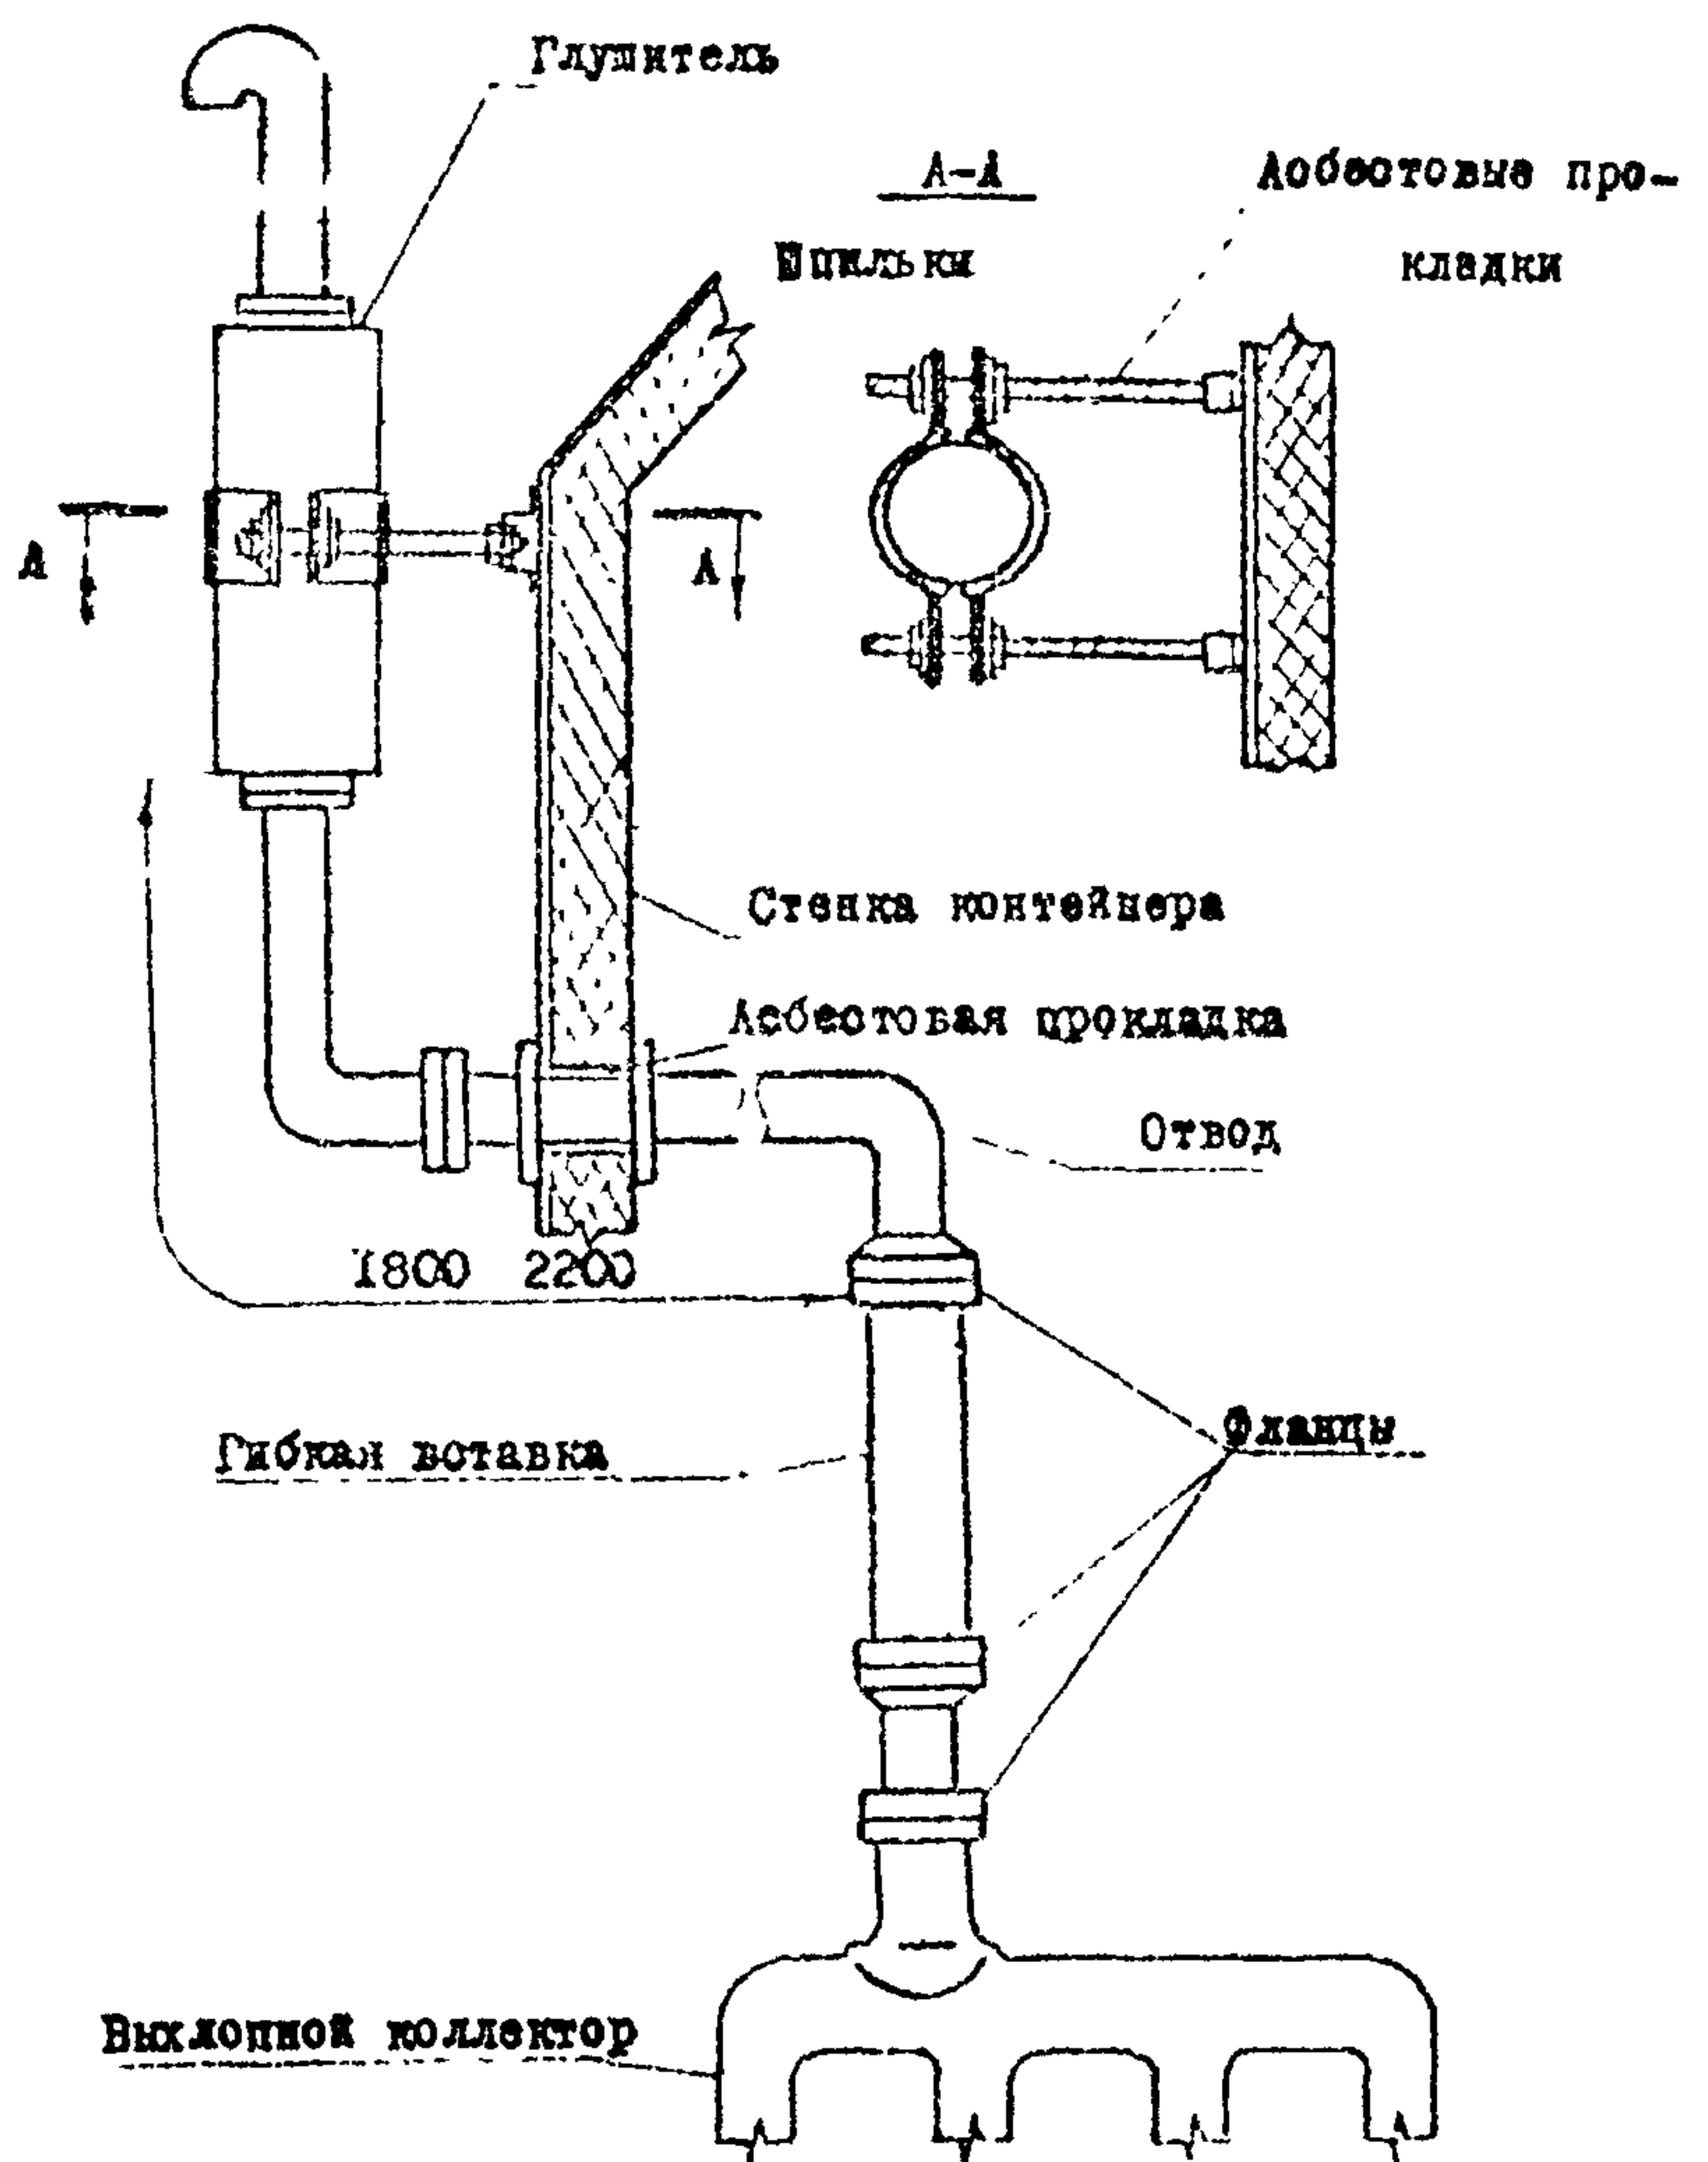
СХЕМА ВЫХЛОПНОГО ТРУБОПРОВОДА
